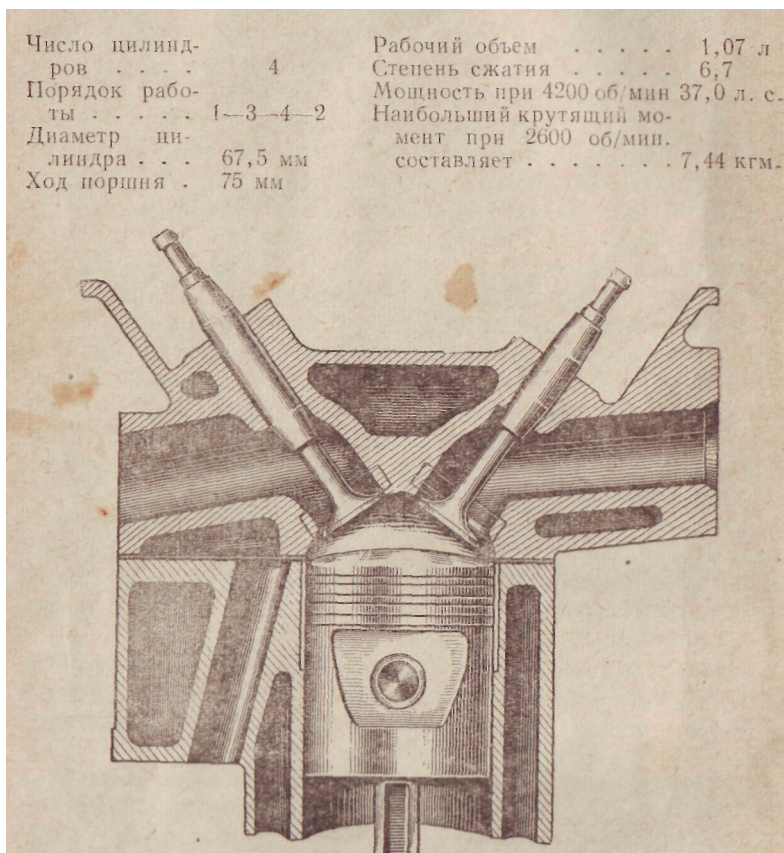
Схема расположения клапанов в верхнеклапанном двигателе со сферической формой камеры сгорания
